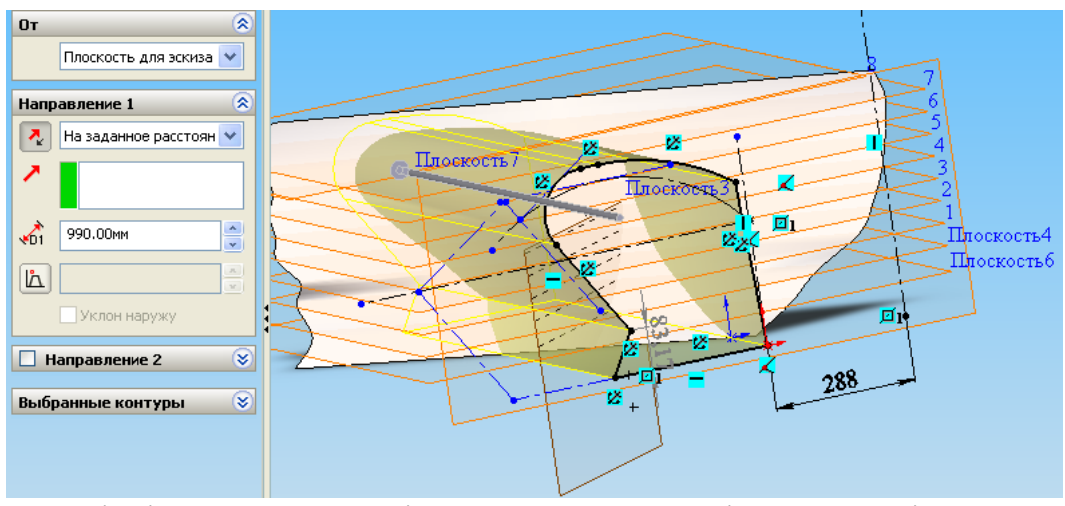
Відсікання поверхні корпусу плуга від поверхні горизонтального циліндра.
